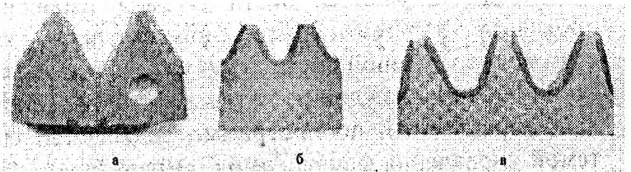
Расположение зоны закалки в сечении зубчатой поверхности шестерен колесной передачи: а - автомобиля МАЗ, б - автомобиля МЗКТ, в, - трактора МТЗ
